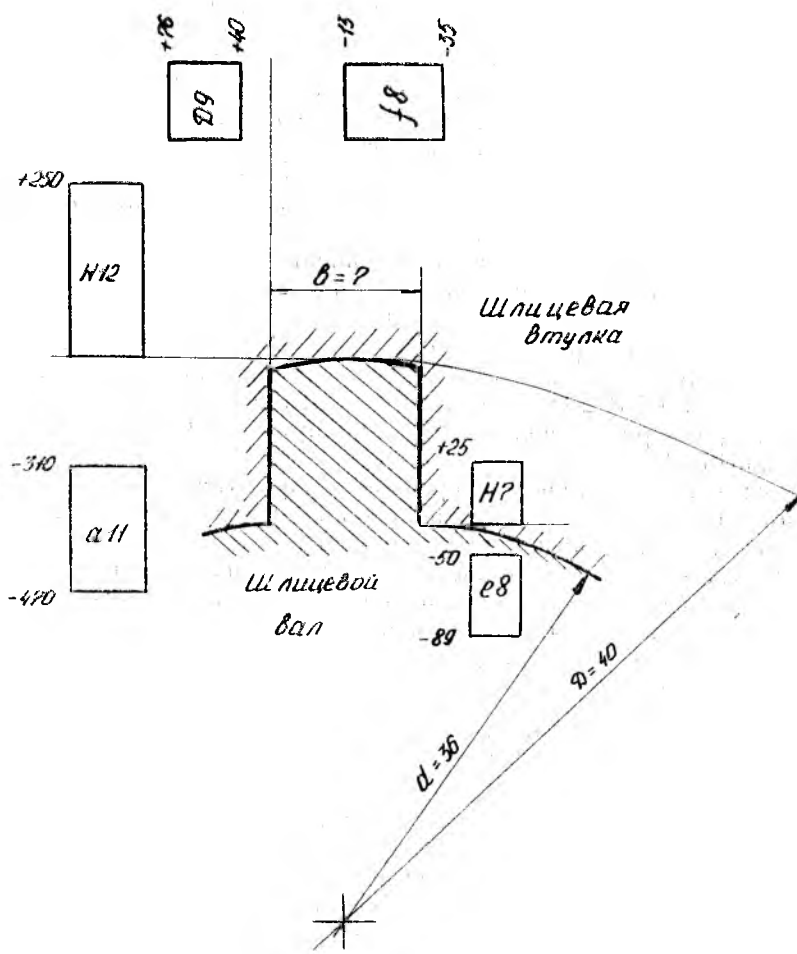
Схема расположения полей допусков шлицевого сопряжения
